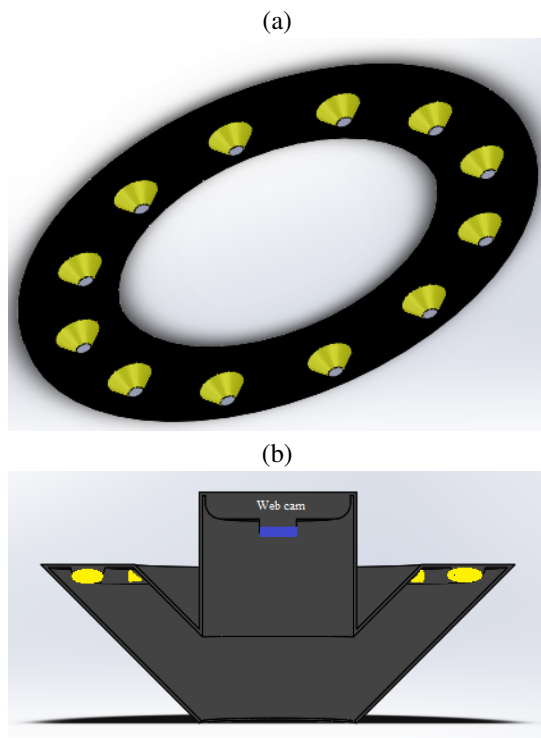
Protótipo do sistema de captação de imagens: (a) iluminante composto por 12 LEDs e (b) estrutura completa com local de fixação da webcam.
